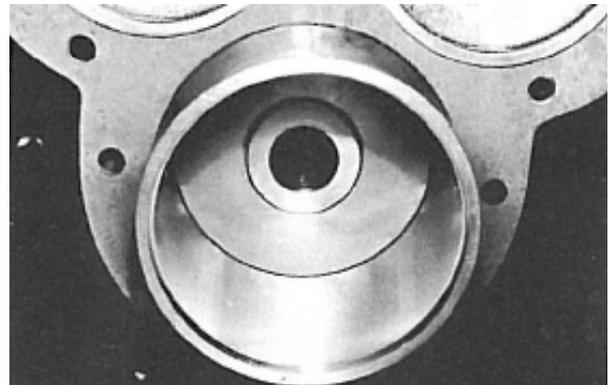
Vue du couvercle d'aspiration; cylindre de décharge, obturateur et piston de décharge installés
